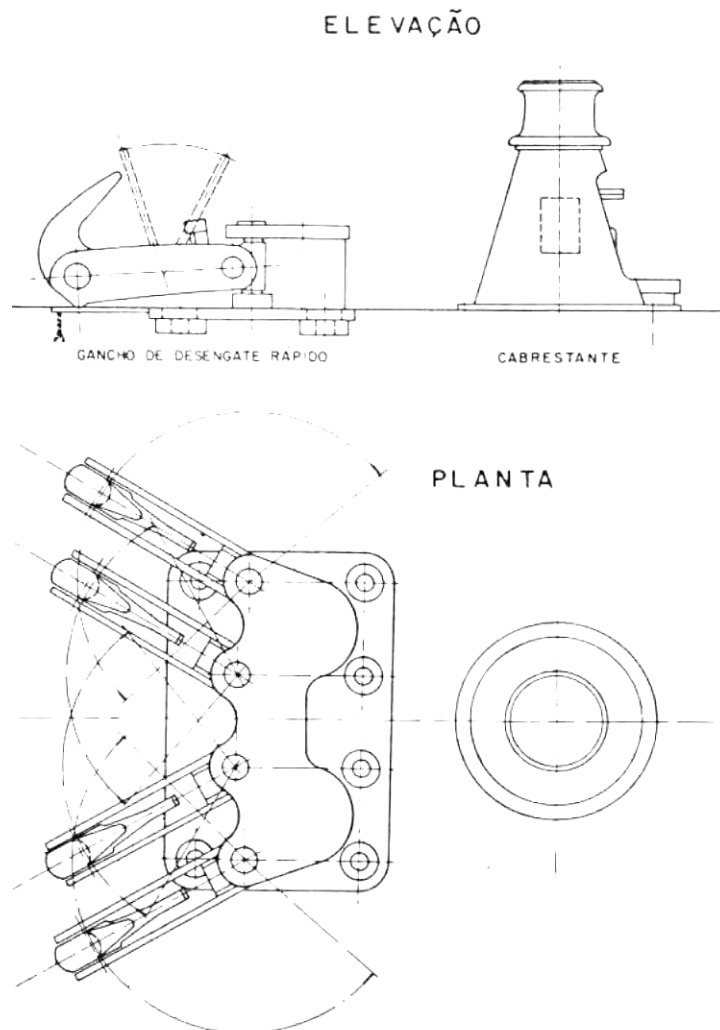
Gancho de Desengate Rápido: Elevação (superior) e Planta [MASON, 1978].
